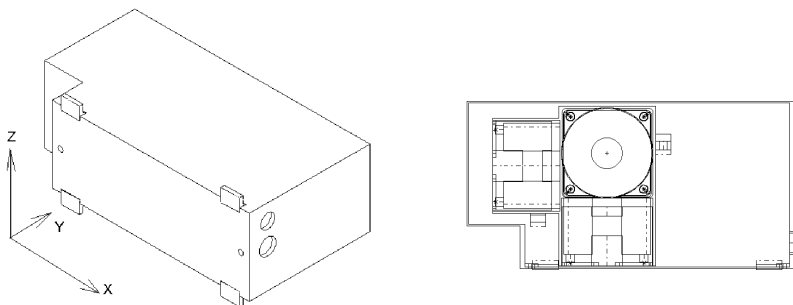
Внешний корпус и размещение блока БИНС в нем.
